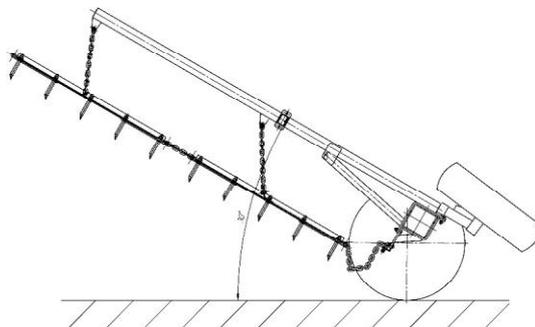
Подъем борон для разворота и очистки зубьев.
